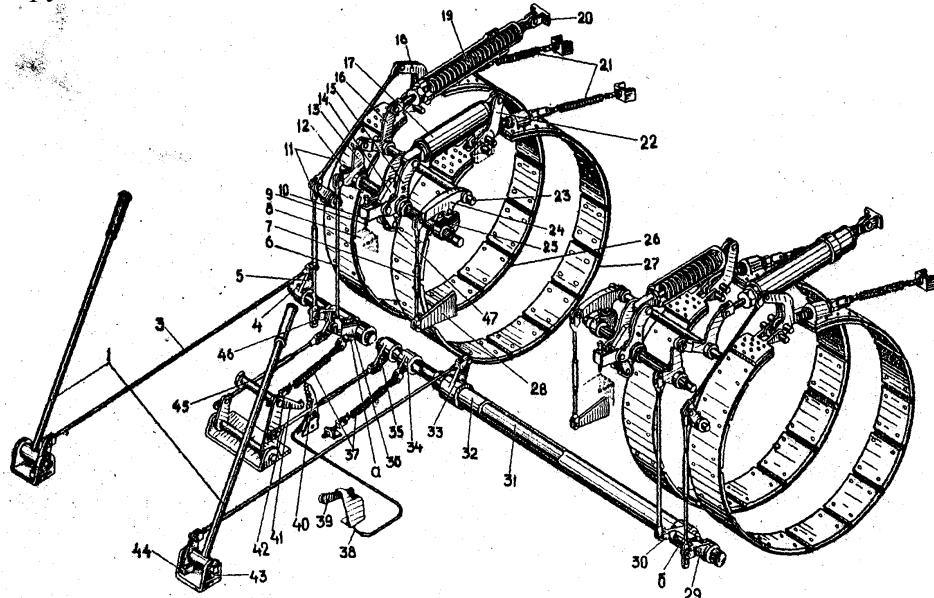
Механізм керування поворотними та зупиночними гальмами:
